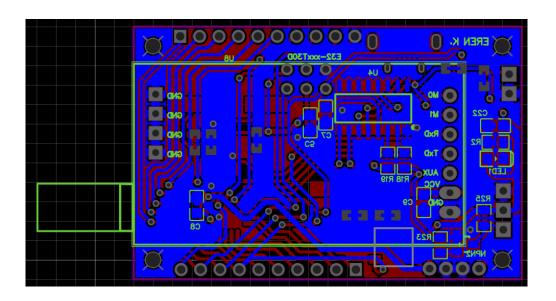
Kumanda Kartı PCB Çizimi (Ön Yüz)
